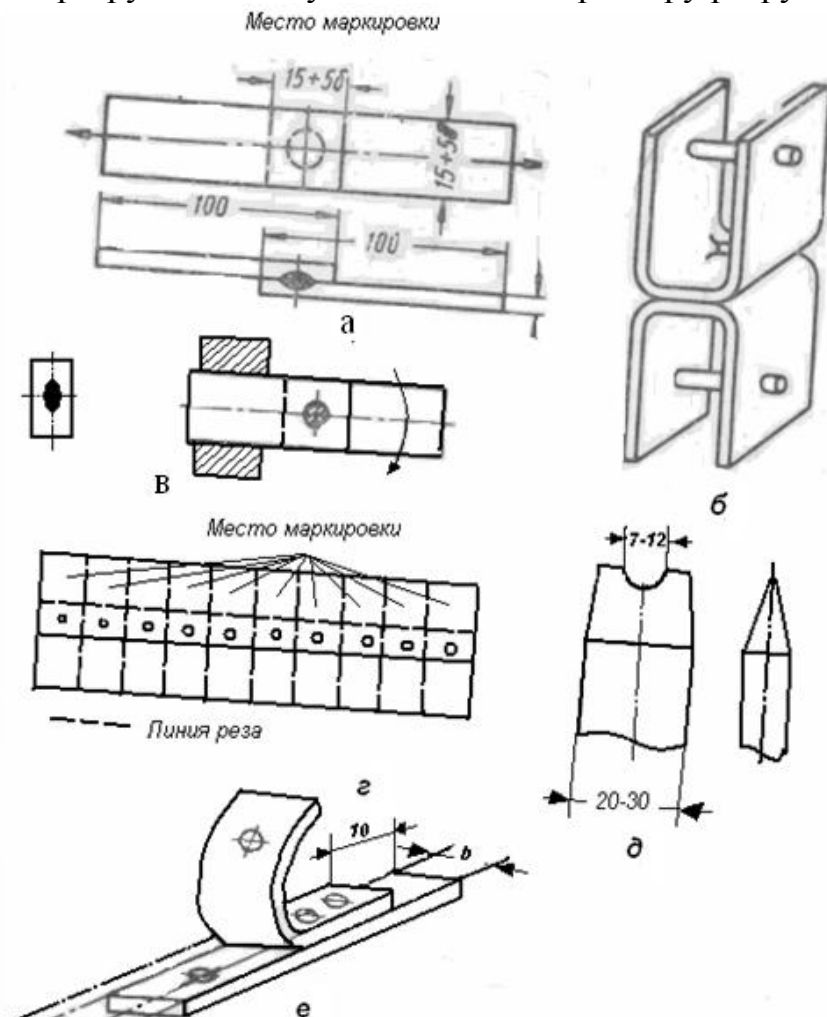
Образцы для испытаний точечной сварки
